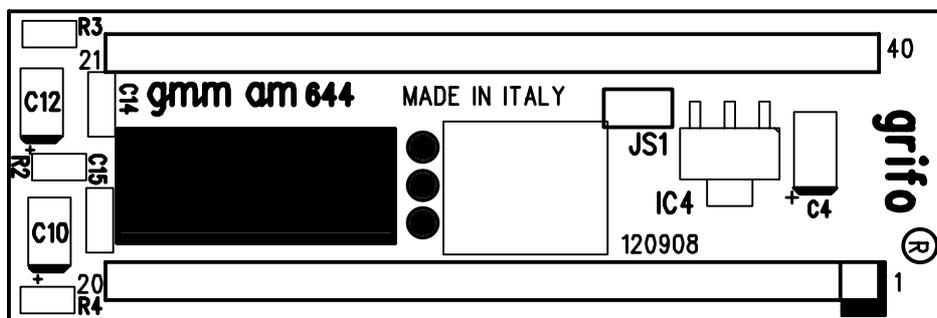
PIANTA COMPONENTI (LATO INFERIORE)
